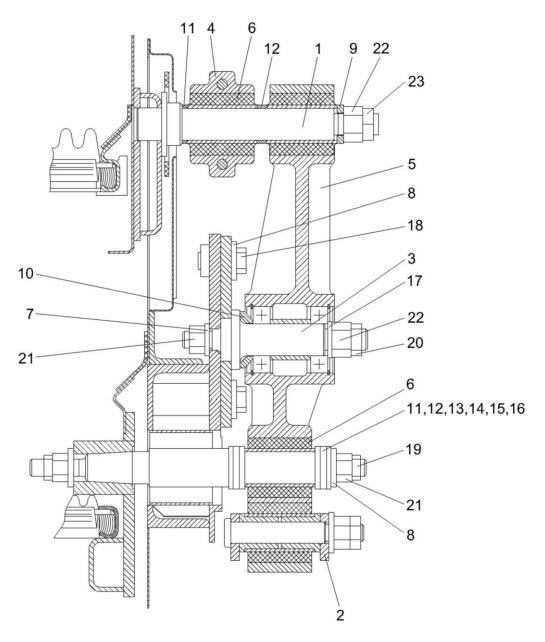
Установка стана решетного верхнего КЗК-10-0260000
